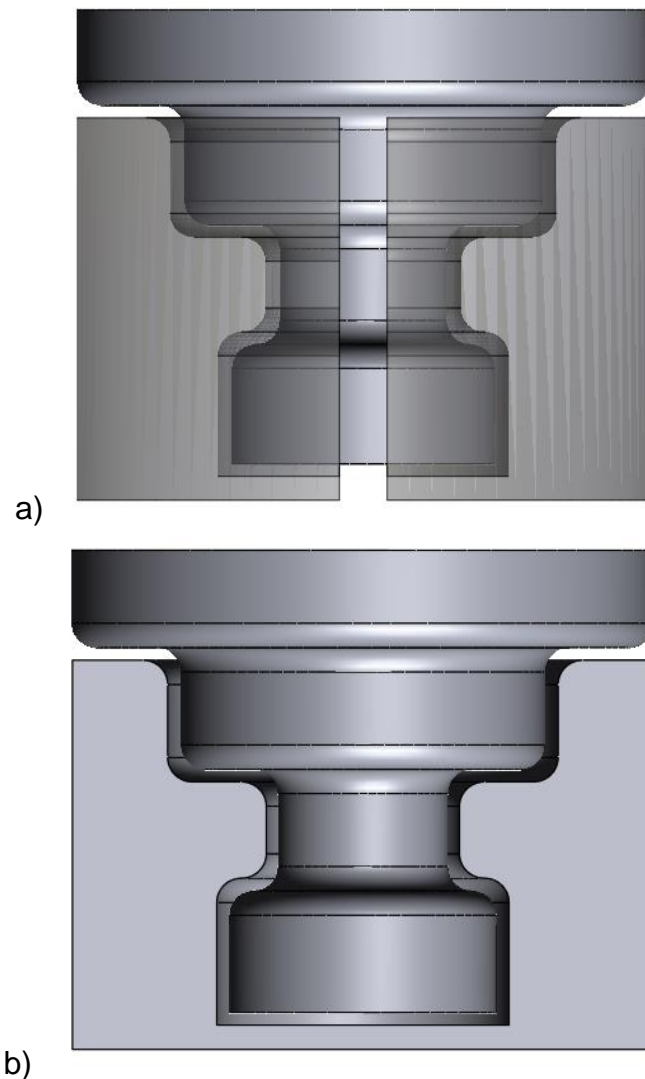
a) Imagen del CAD de la pieza 7 con el soporte empleado para su fabricación en la que se puede apreciar el espacio libre entre ambas partes; b) Imagen del CAD de la pieza 7 con una de las 2 partes que forman el soporte de la pieza 7 colocados en la misma posición en la que serían impresos.
